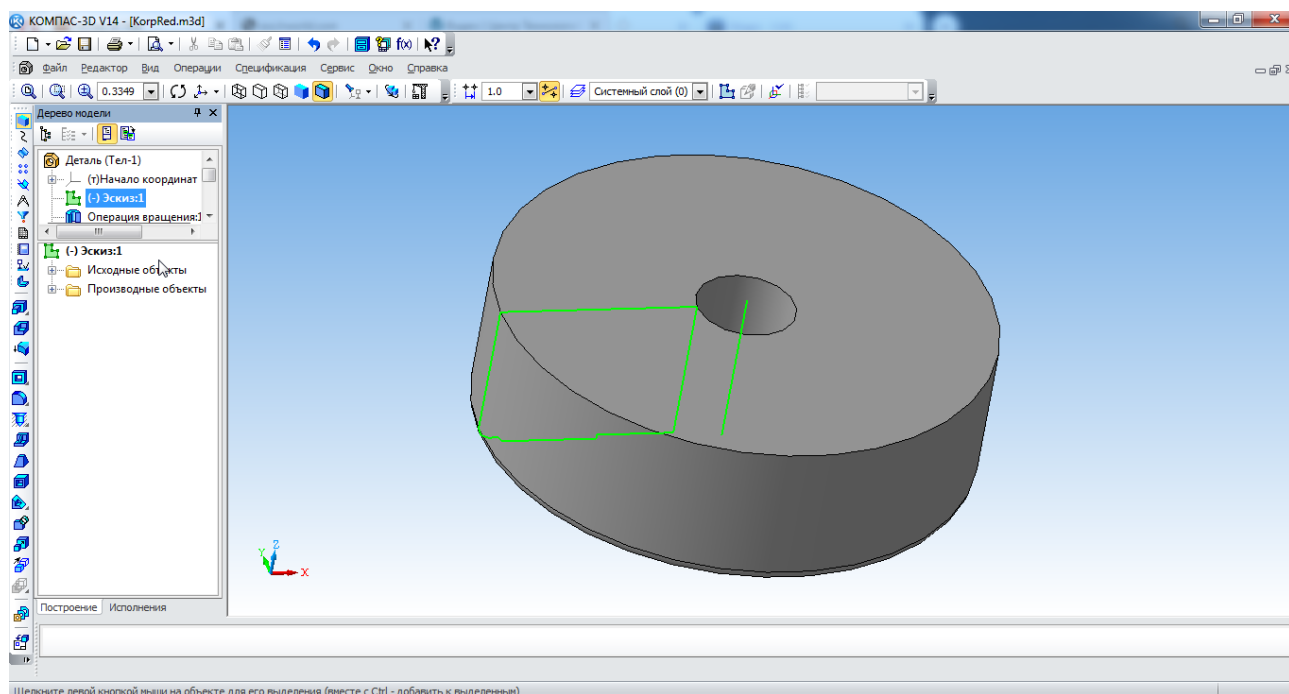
Створення заготовки корпусу для шестерні редуктора
